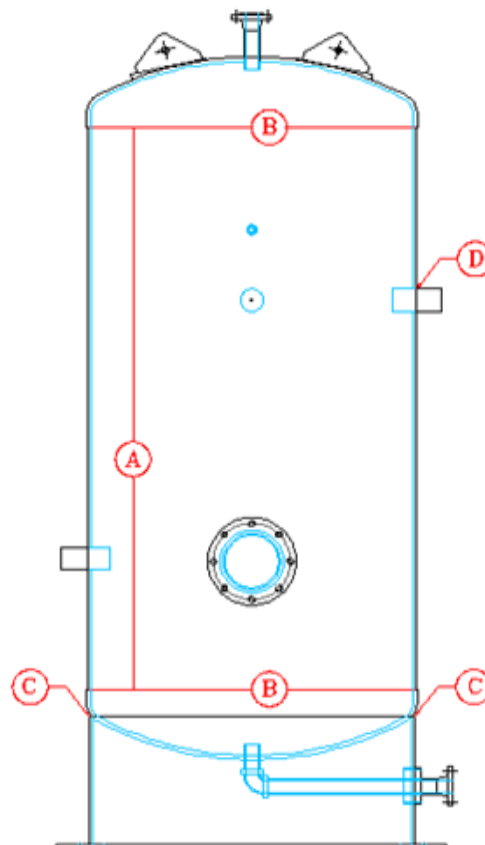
Cordones de Soldadura en el recipiente
